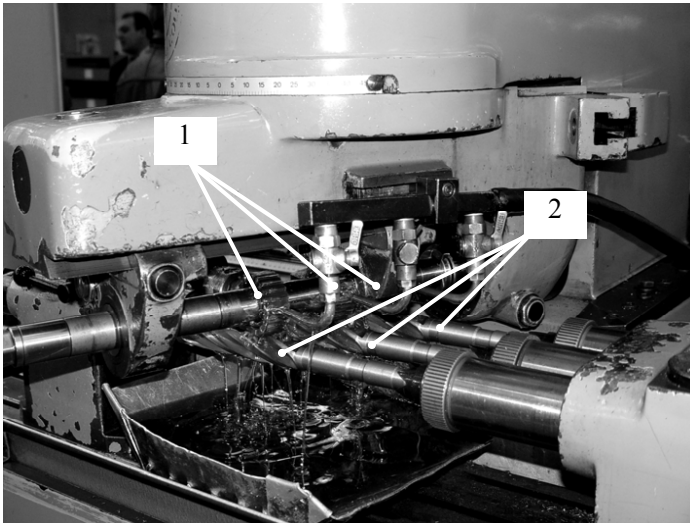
Одновременное фрезерование спинок на трех заготовках сверл:
